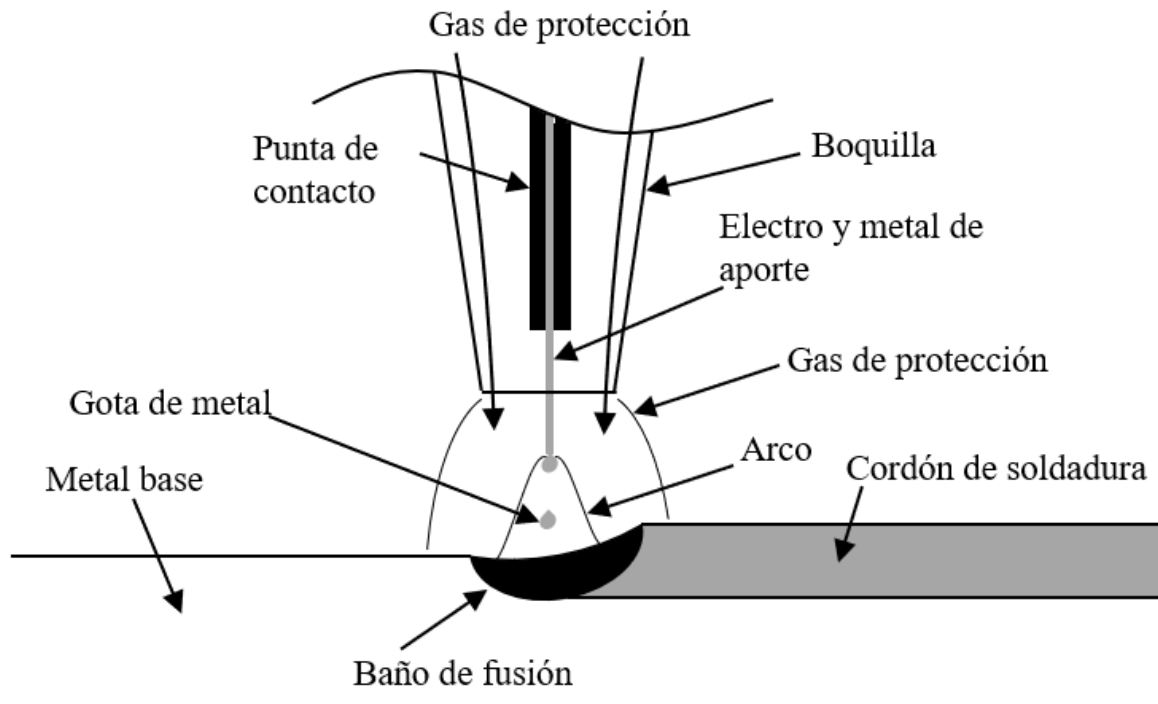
Esquema general de los elementos básicos en la soldadura al arco.
